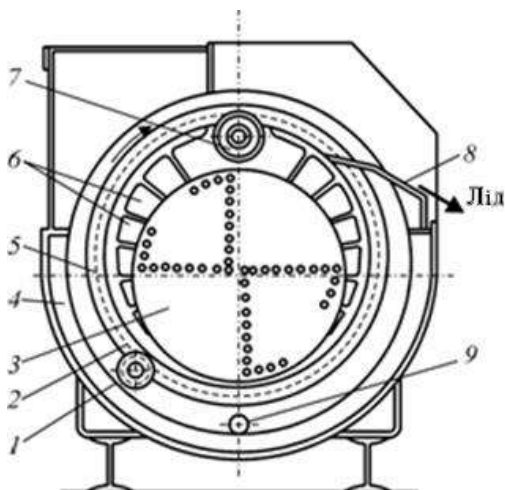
Схема генератора лускатого льоду з горизонтальним барабаном конструкції Г. Фільда: 1 – шестерня приводу барабана; 2 – зубчастий вінець барабана; 3 – кожухотрубний випарник-охолоджувач розсолу; 4 – ізоляція; 5 – гнучка металева обичайка барабана наморожування; 6 – канали для циркуляції розсолу в сорочці охолодження гнучкої обичайки; 7 – деформуючий ролик; 8 – шкребок для знімання льоду; 9 – трубопровід подачі води у водяну ванну
